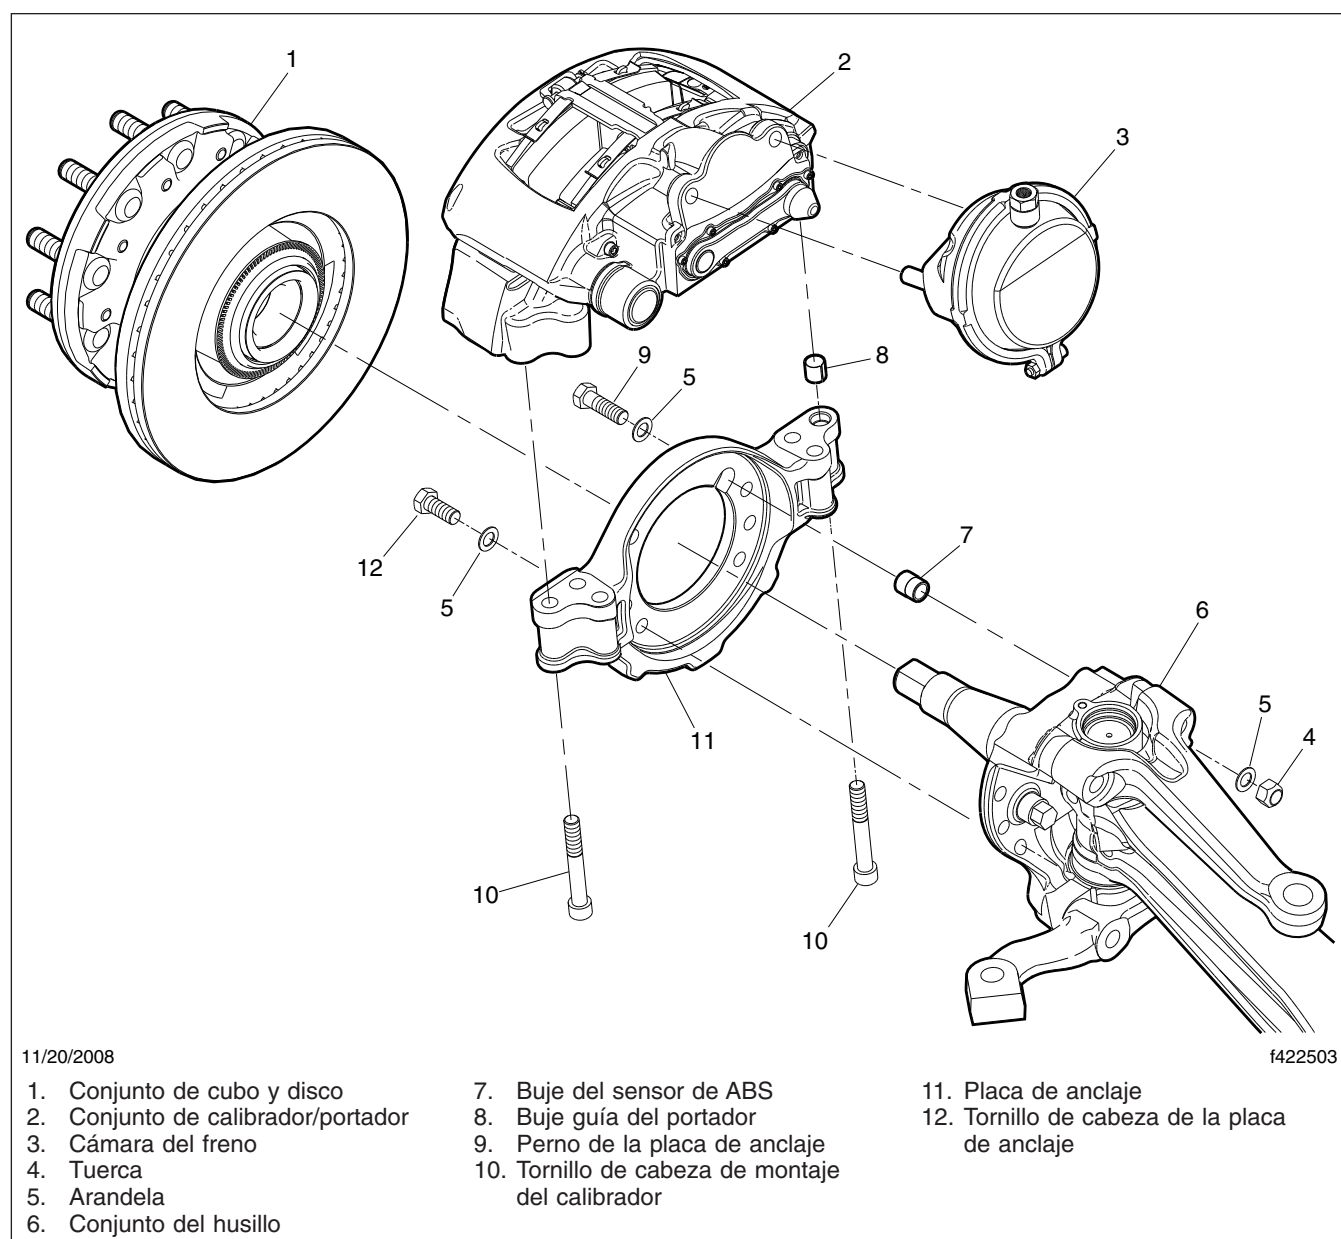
, Instalación del conjunto de calibrador y portador delanteros
